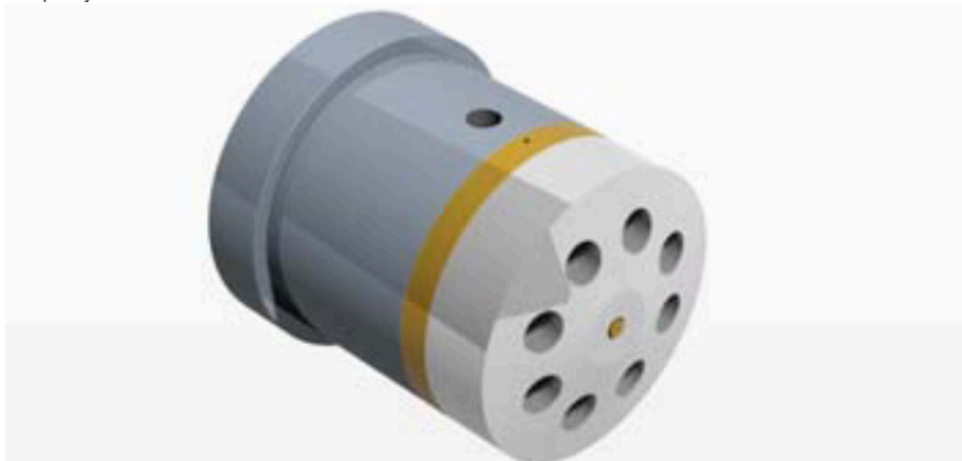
Vista en isométrico del ensamblaje generado en Solid Edge.
